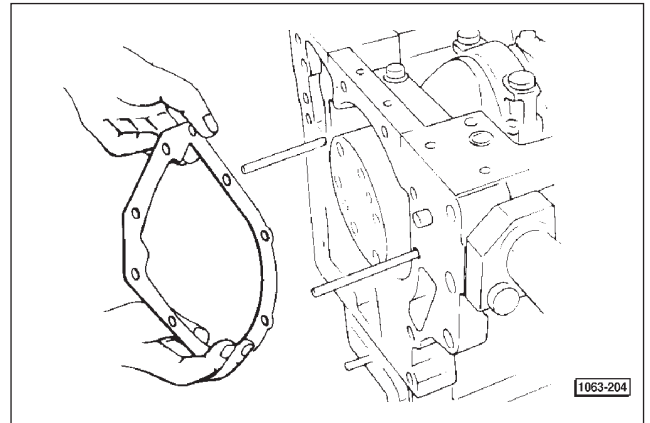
Die Dichtung des hinteren Flansches der Kurbelwelle anbringen.
